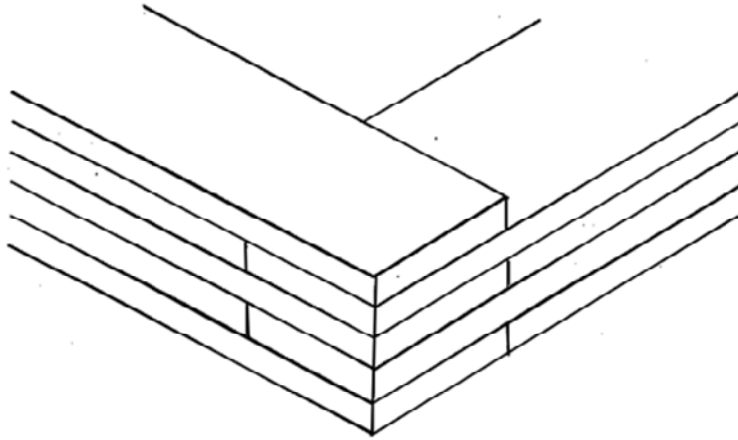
Disposition des tôles en joints à double recouvrement.
